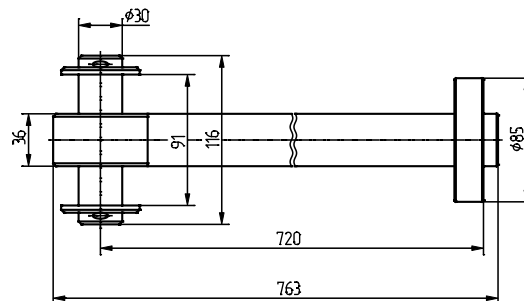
Соединительная тяга для механизмов МЗО-10000-97К (в комплекте - вилка и шток)
